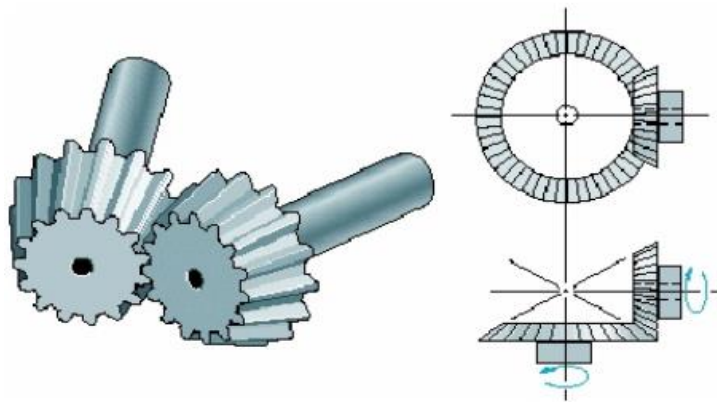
Engrenagens cónicas de dentes retos [16]
